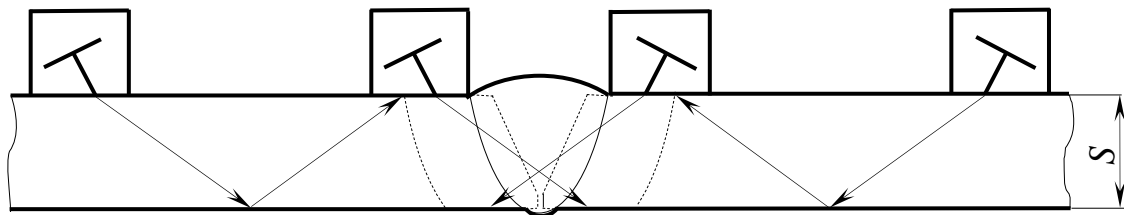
Схема контроля стыковых сварных соединений, выполненных односторонней сваркой
